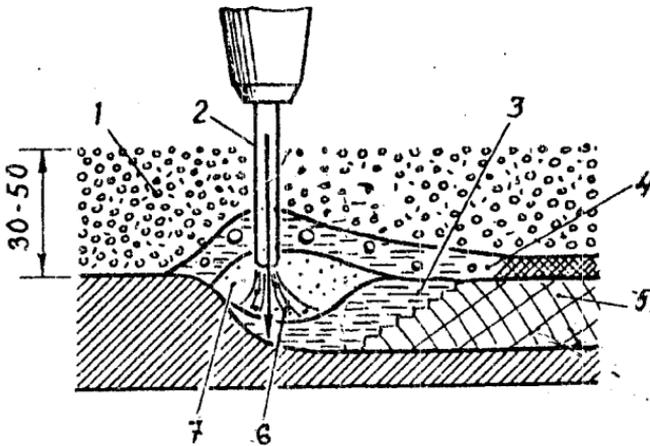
Схема горіння дуги зварювання під флюсом:
